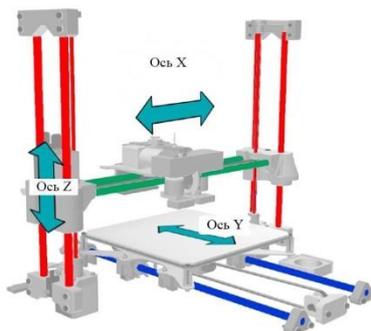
Пример 3 – осевого станка для послойного наплавления
